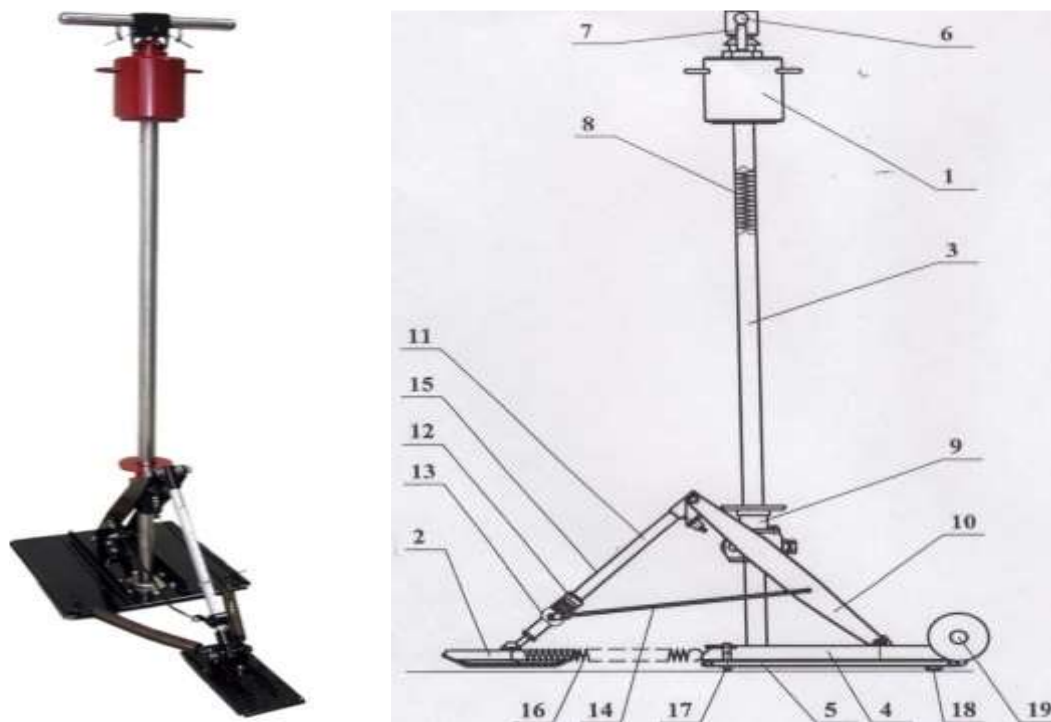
Внешний вид и конструктивное устройство измерителя коэффициента сцепления портативного ИКСп-2М: 1 - груз; 2 – башмак; 3 – штанга; 4 – кронштейн; 5 – основание; 6 – рукоятка; 7 - механизм фиксации; 8 – пружина; 9 – ползун; 10 – кулиса; 11 – рычаг; 12 - кольцо-указатель; 13 – втулка; 14 – тяга; 15 – шкала; 16 - пружина возвратная; 19 - опора регулируемая; 20 - опора нерегулируемая; 21 – колесо.
